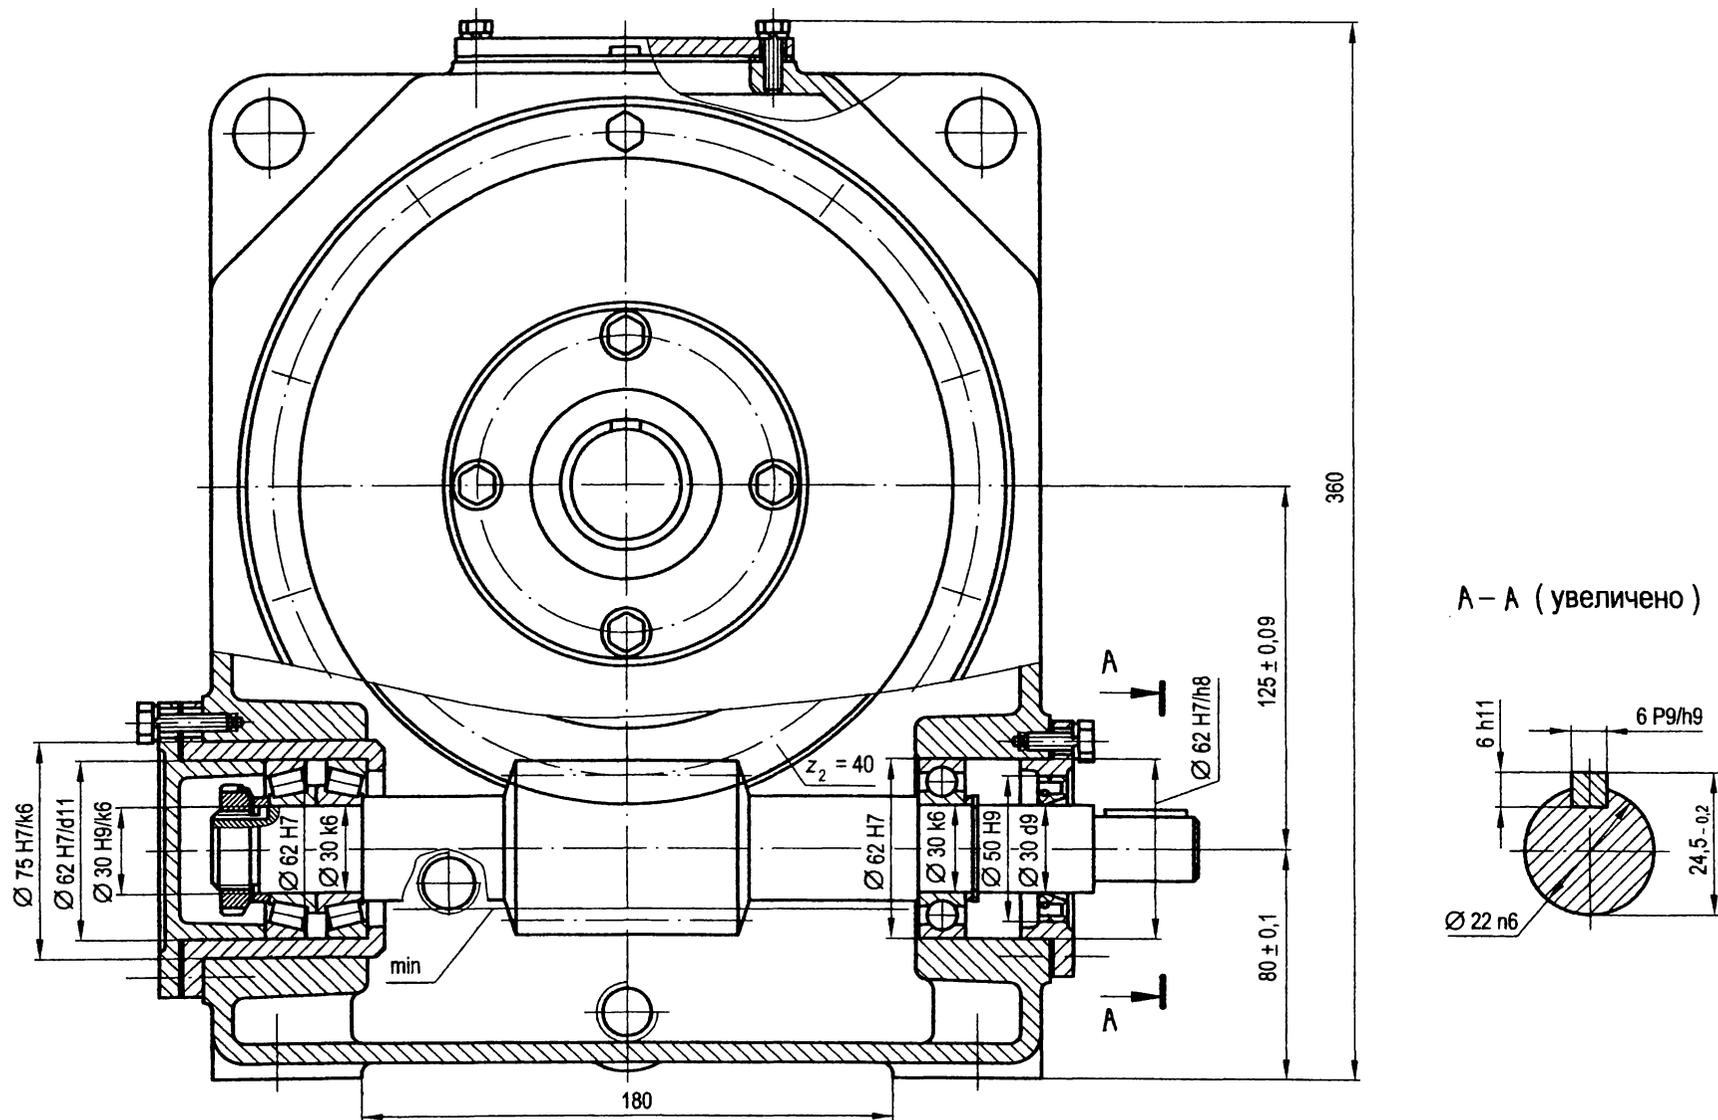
Быстроходный (входной) вал – червяк редуктора с червячной передачей (червяк расположен горизонтально под червячным колесом)
